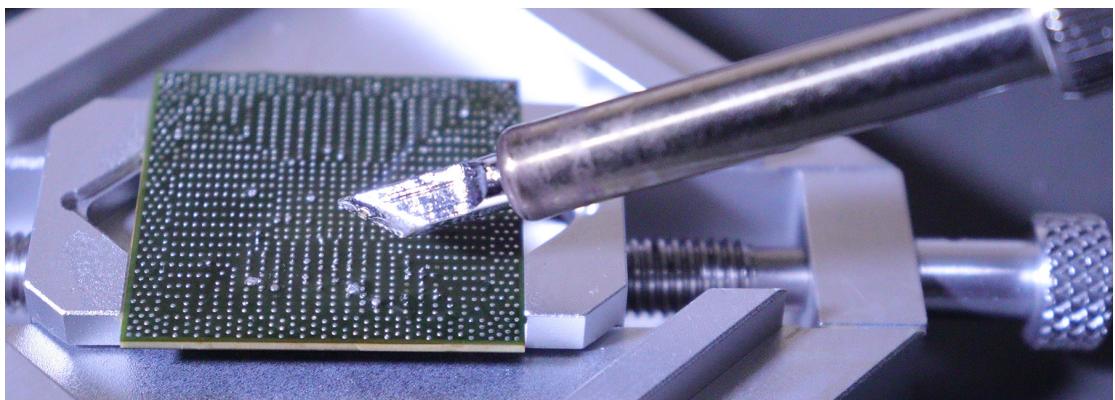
remoção do excesso de solda com o ferro de soldar e ponteira do tipo faca
